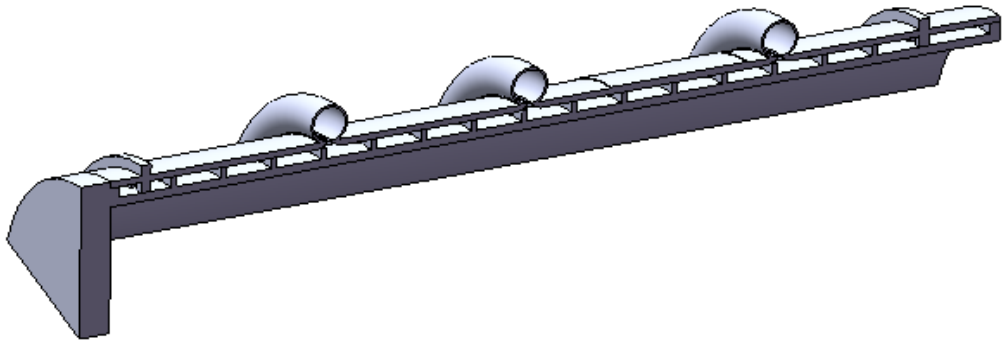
Расчетная геометрическая схема первого варианта конструкции жаровой трубы
